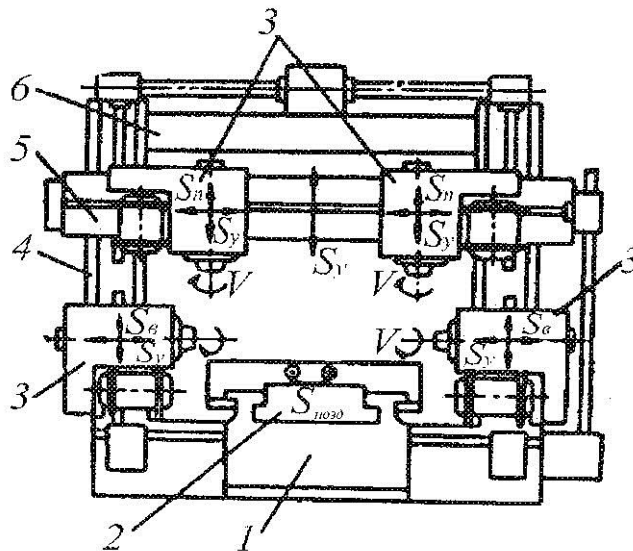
Загальний вид поздовжньо-фрезерного верстата з двома стояками
